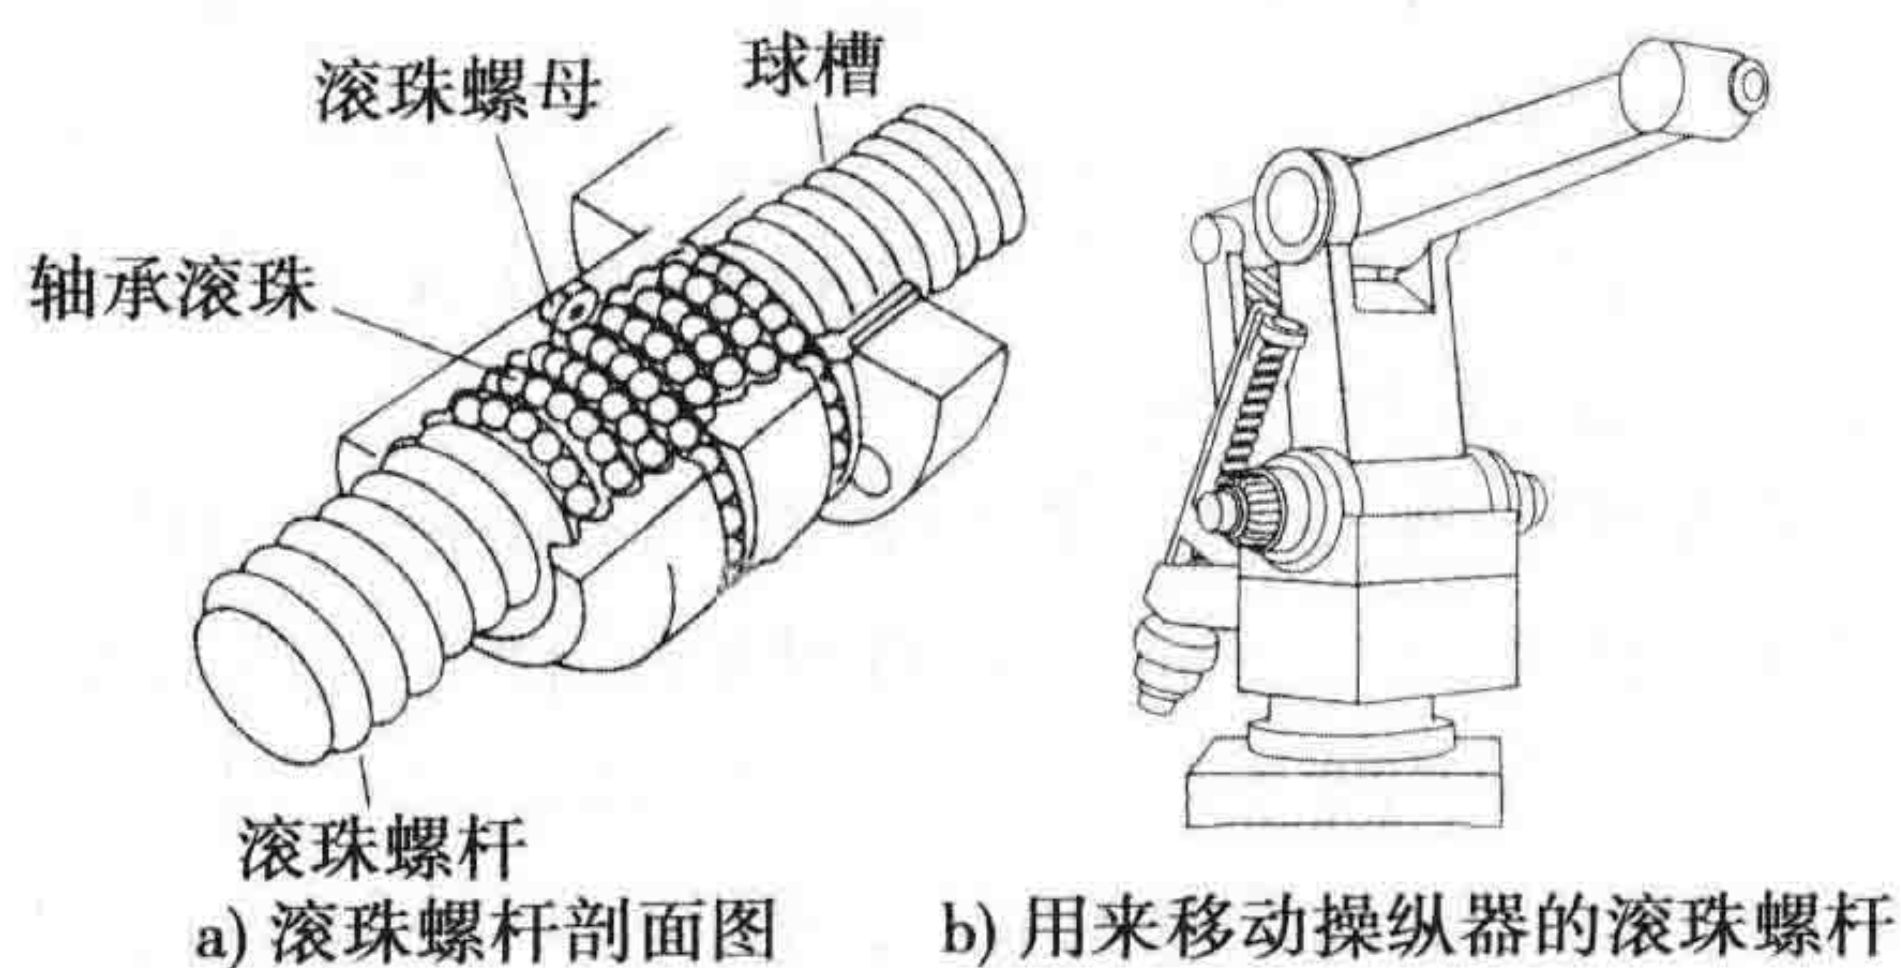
滚珠螺杆 (Warner Clutch and Brake Co. 产品)
